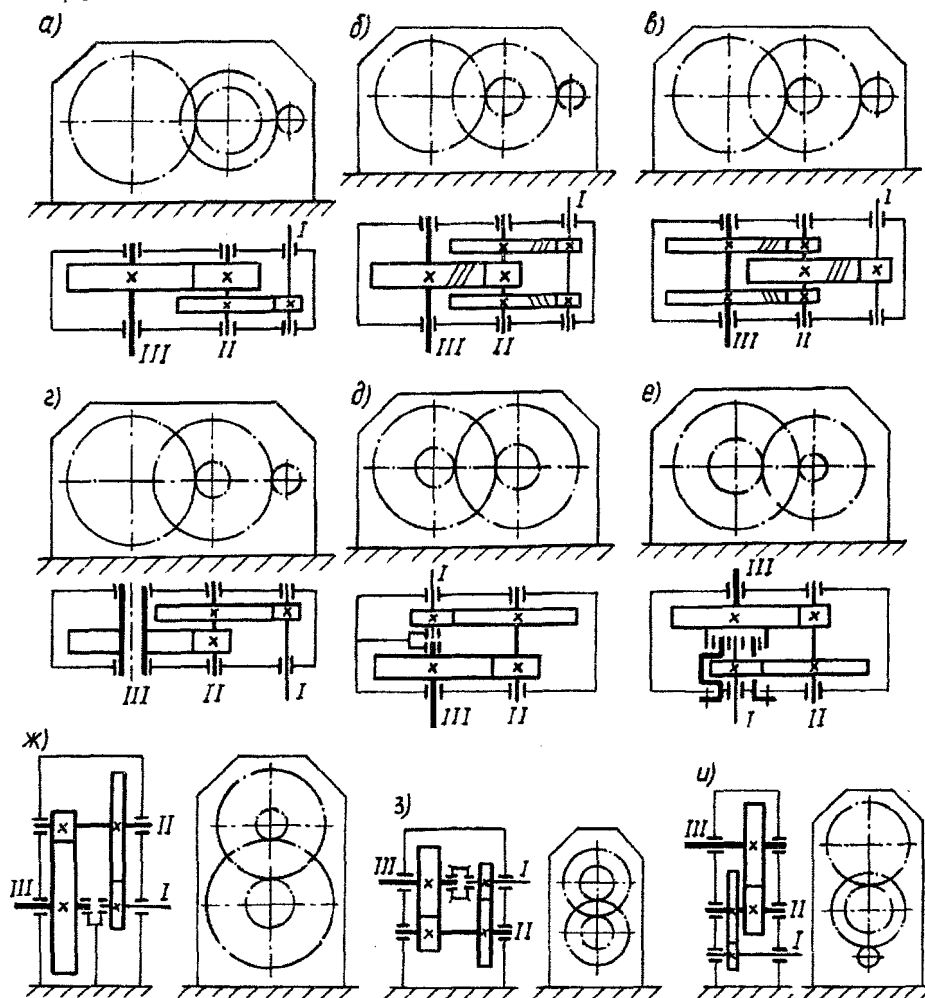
Кинематические схемы двухступенчатых цилиндрических редукторов: I - быстроходный вал; II - промежуточный вал; III - тихоходный вал
